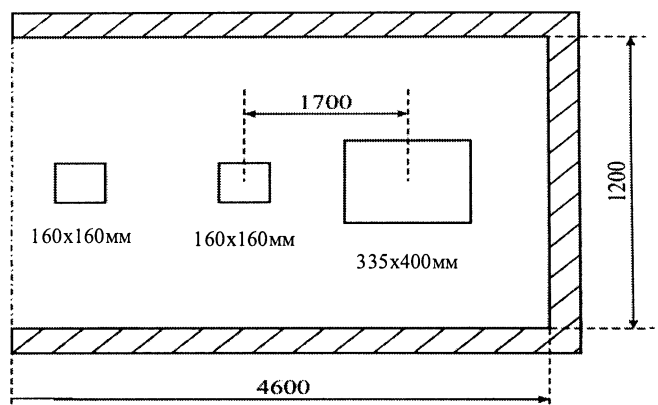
Схема промежуточного ковша шестиручьевого МНЛЗ ДМК
